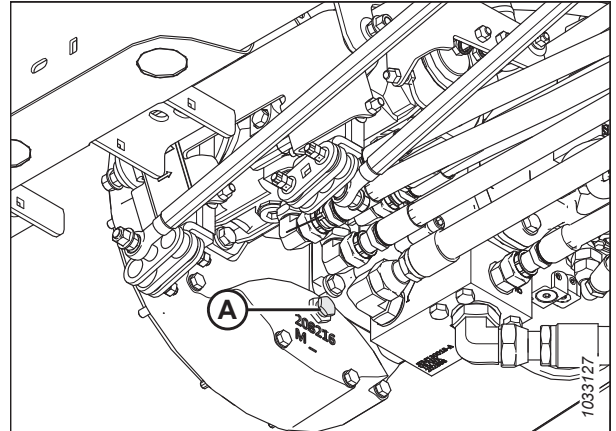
Getriebeschmiermittel-Kontrollschraube
